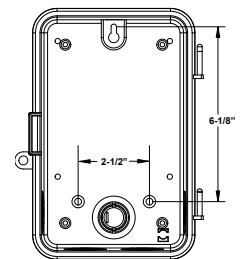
Vue arrière du boîtier et dimensions des orifices de montage
